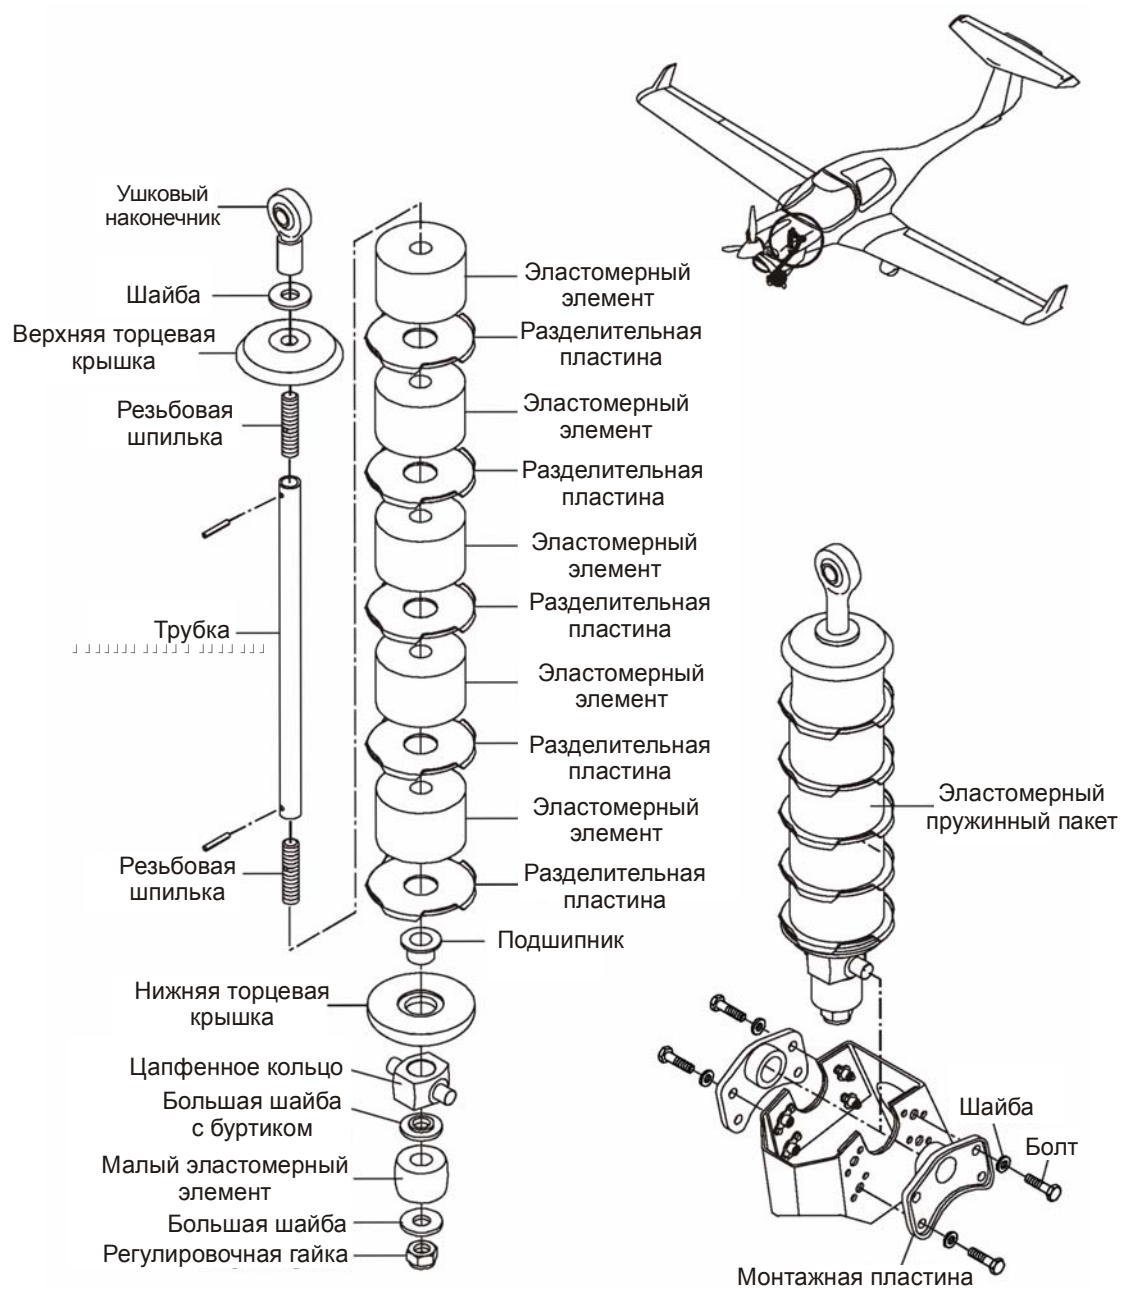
Эластомерный пружинный пакет с узлом крепления
